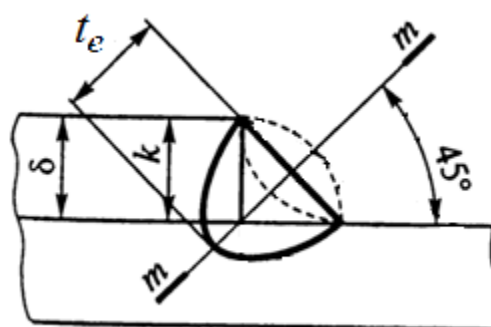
Эффективная толщина сварного шва.
